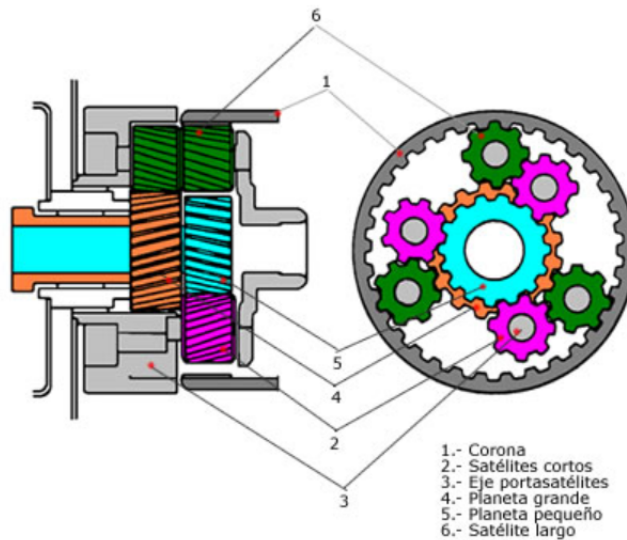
Esquema de engranaje Ravigneaux [8].
